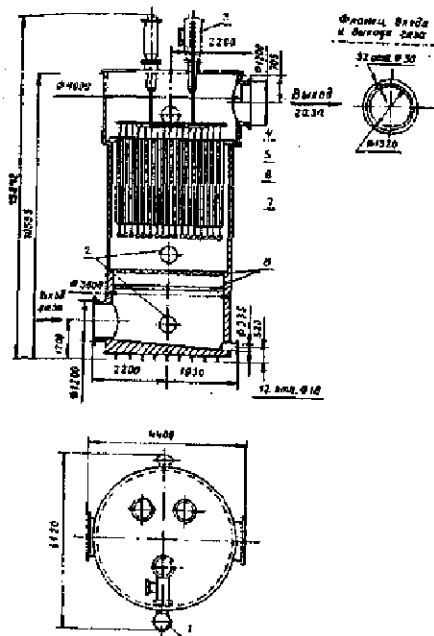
Мокрый электрофильтр типа ЭВМ: 1 - защитная коробка для подвода тока; 2 - люк обслуживания; 3 - изоляторная коробка; 4 - коронирующий электрод; 5 - осадительный электрод; 6 - корпус; 7 - футеровка корпуса; 8 - газораспределительная решетка.
